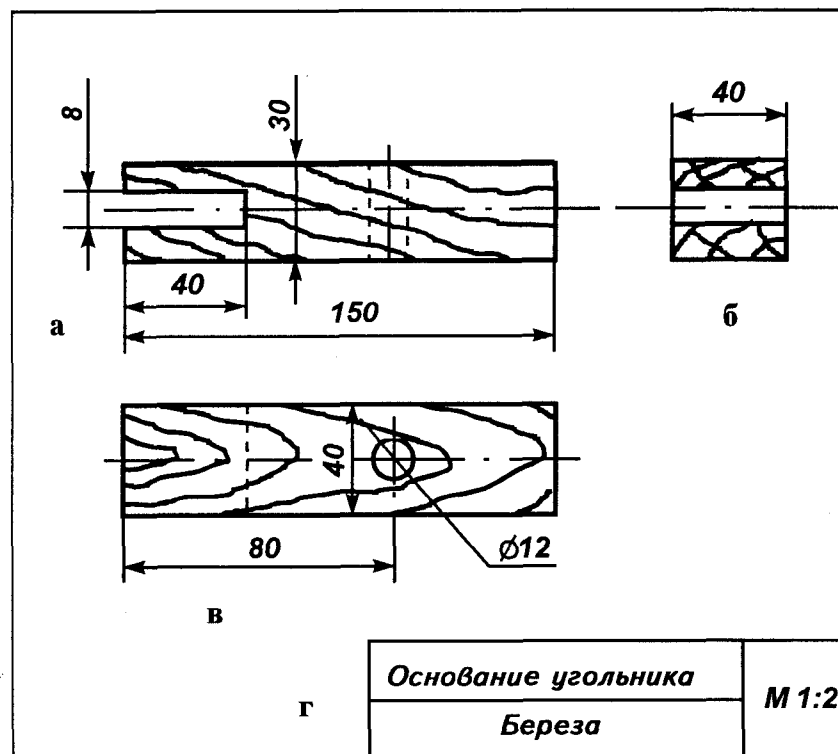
Чертеж призматической детали: а — главный вид; б — вид слева; в — вид сверху; г — основная надпись
